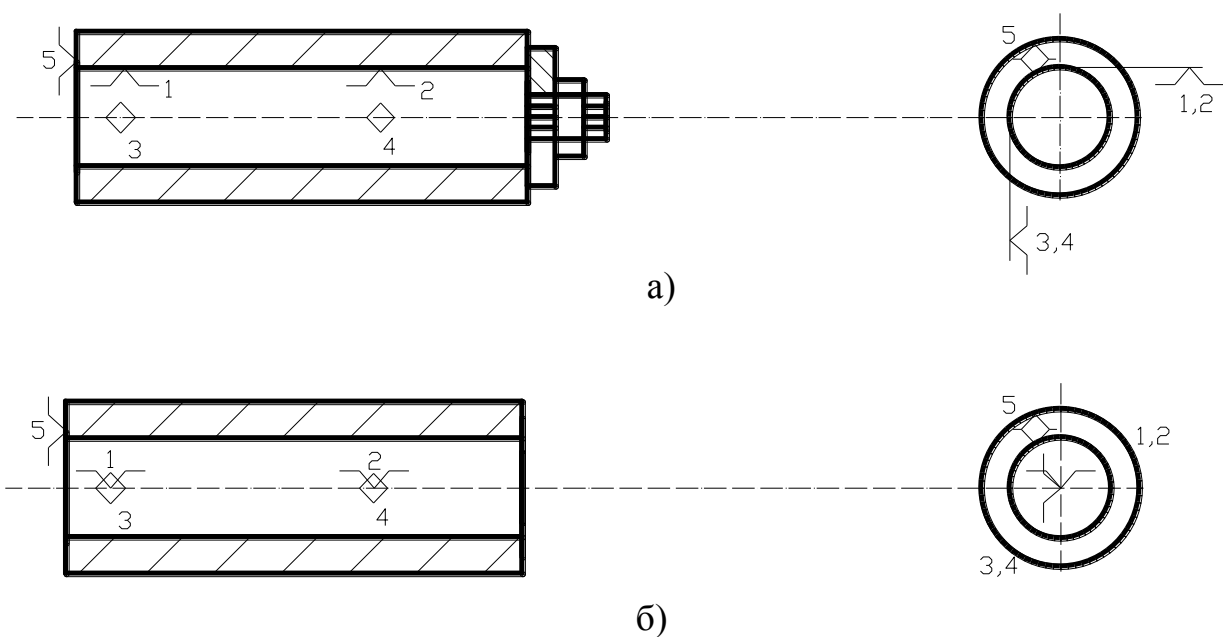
Базування втулок на чистові технологічні бази при обробці поверхонь обертання:
